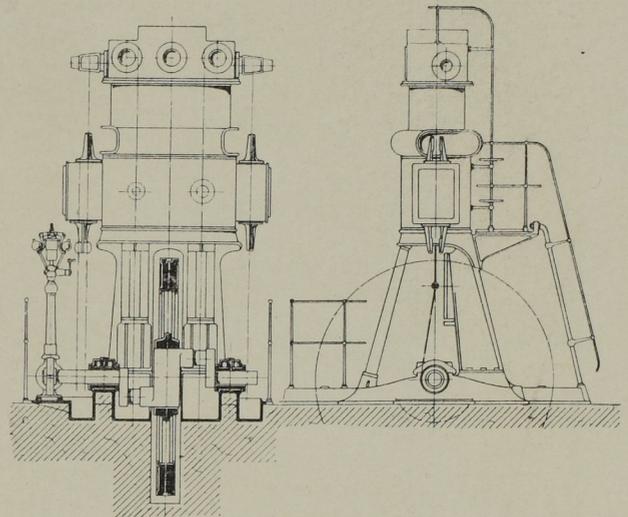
Stirnansicht. Abb. 103. Seitenansicht.
